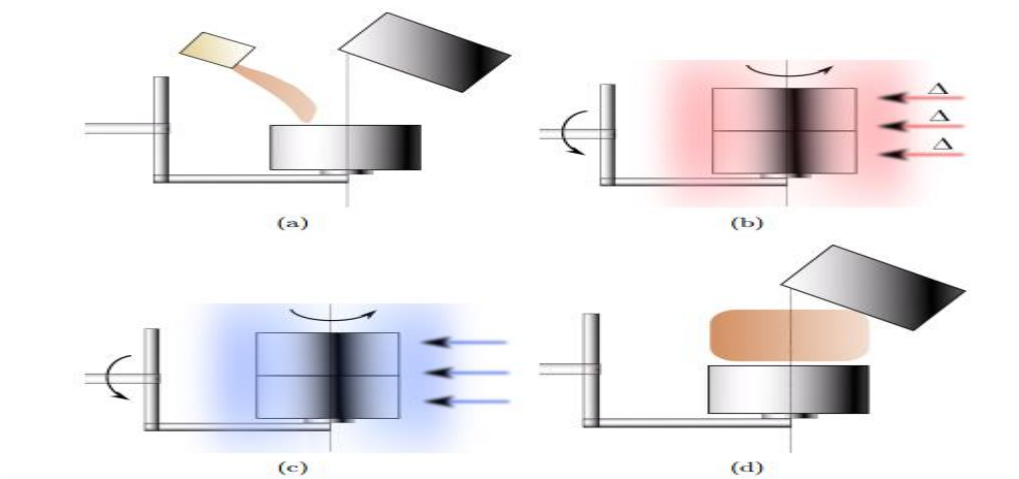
Etapes principales du roto moulage : chargement (a), mise en rotation biaxiale et chauffage (b), refroidissement (c), démoulage (d)
